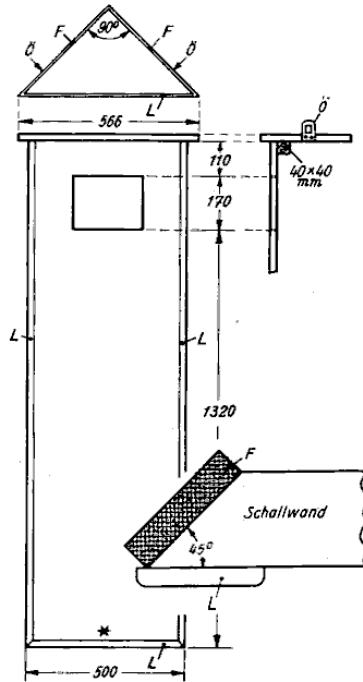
Aufriß einer Wand für ein Lautsprechergehäuse, die mit Sand gefüllt wird
